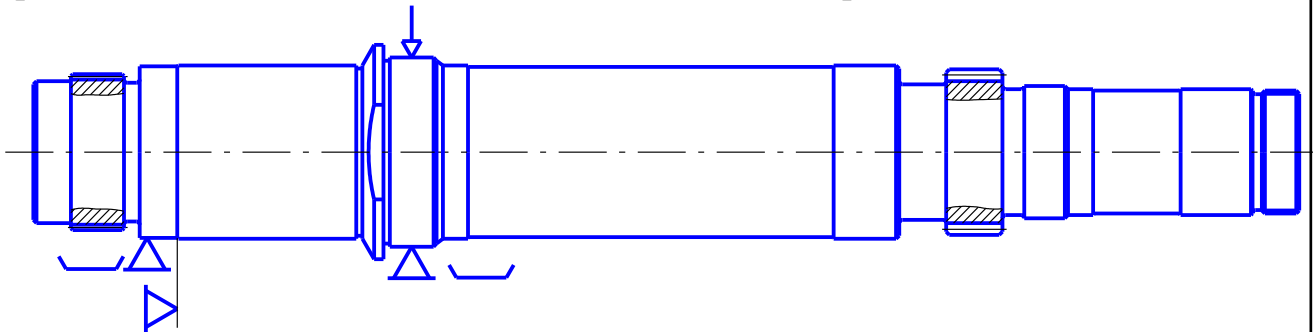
Установка вала на призмі з упором у торець (фрезерна операція)
